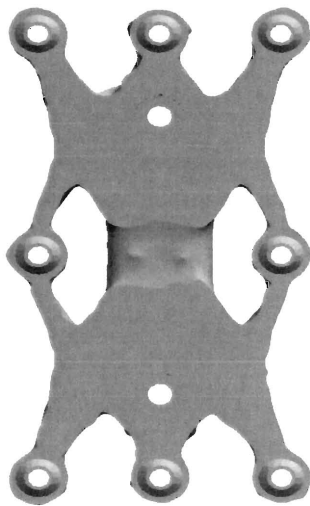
Vedere frontală element de prindere optimizat topologic CAD – TIP 2
